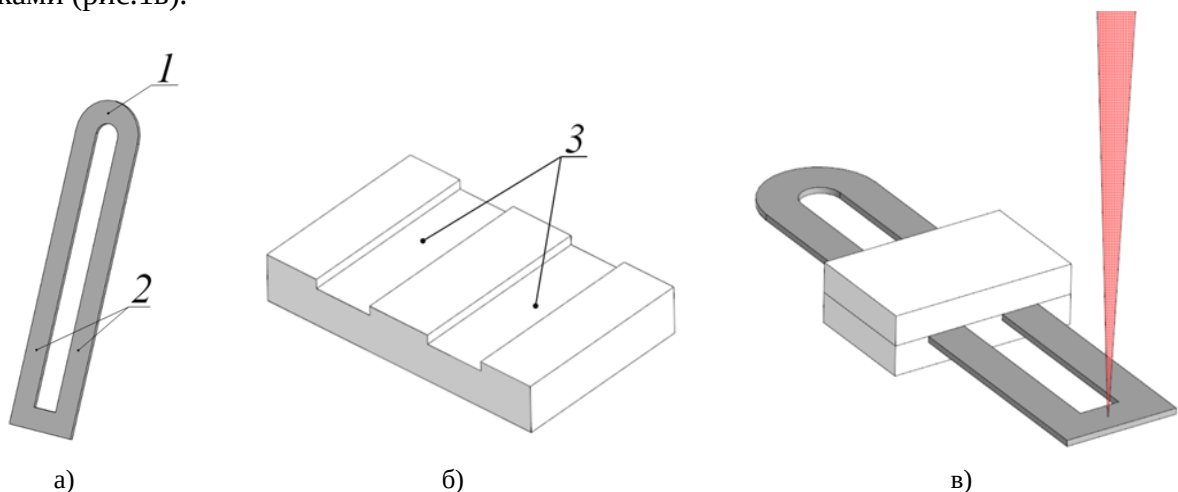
Последовательность изготовления ПТЭК: а) – U-образная дуга (1 – вершина дуги; 2 – ножки дуги); б) – диэлектрическая пластина с пазами (3); в) - катод в сборе.
